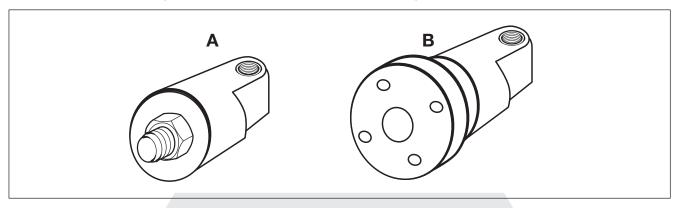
Varianten für die Befestigung an die Maschinenwelle
